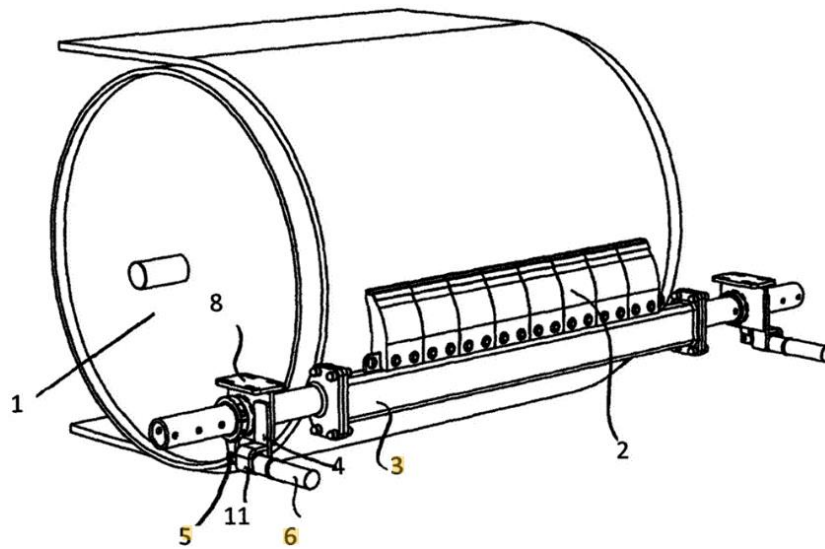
Модернізований вузол очищувача стрічки
